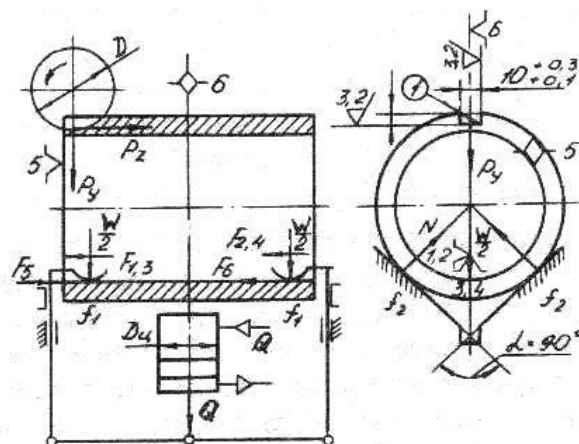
Принципіальна розрахункова схема пристосування для фрезерування пазу
